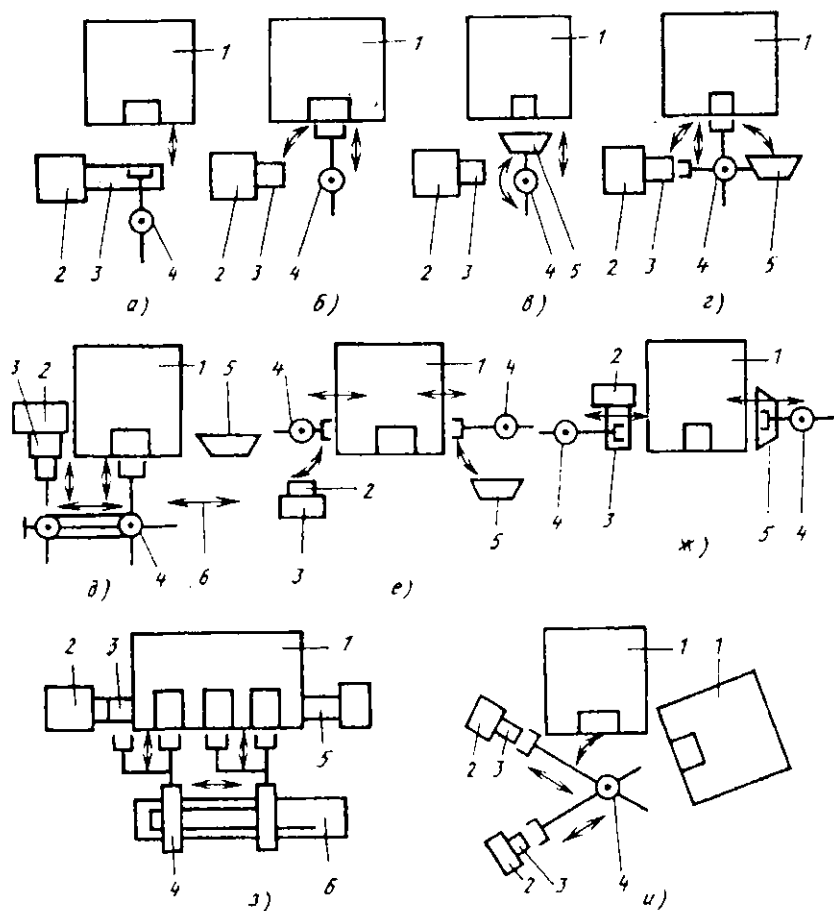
Типовые структуры РТК листовой штамповки мелких деталей: 1 — пресс; 2 — устройство подачи заготовок; 3 — позиция базирования заготовок; 4 — ПР; 5 — устройство приема деталей; 6 — транспортное устройство ПР
